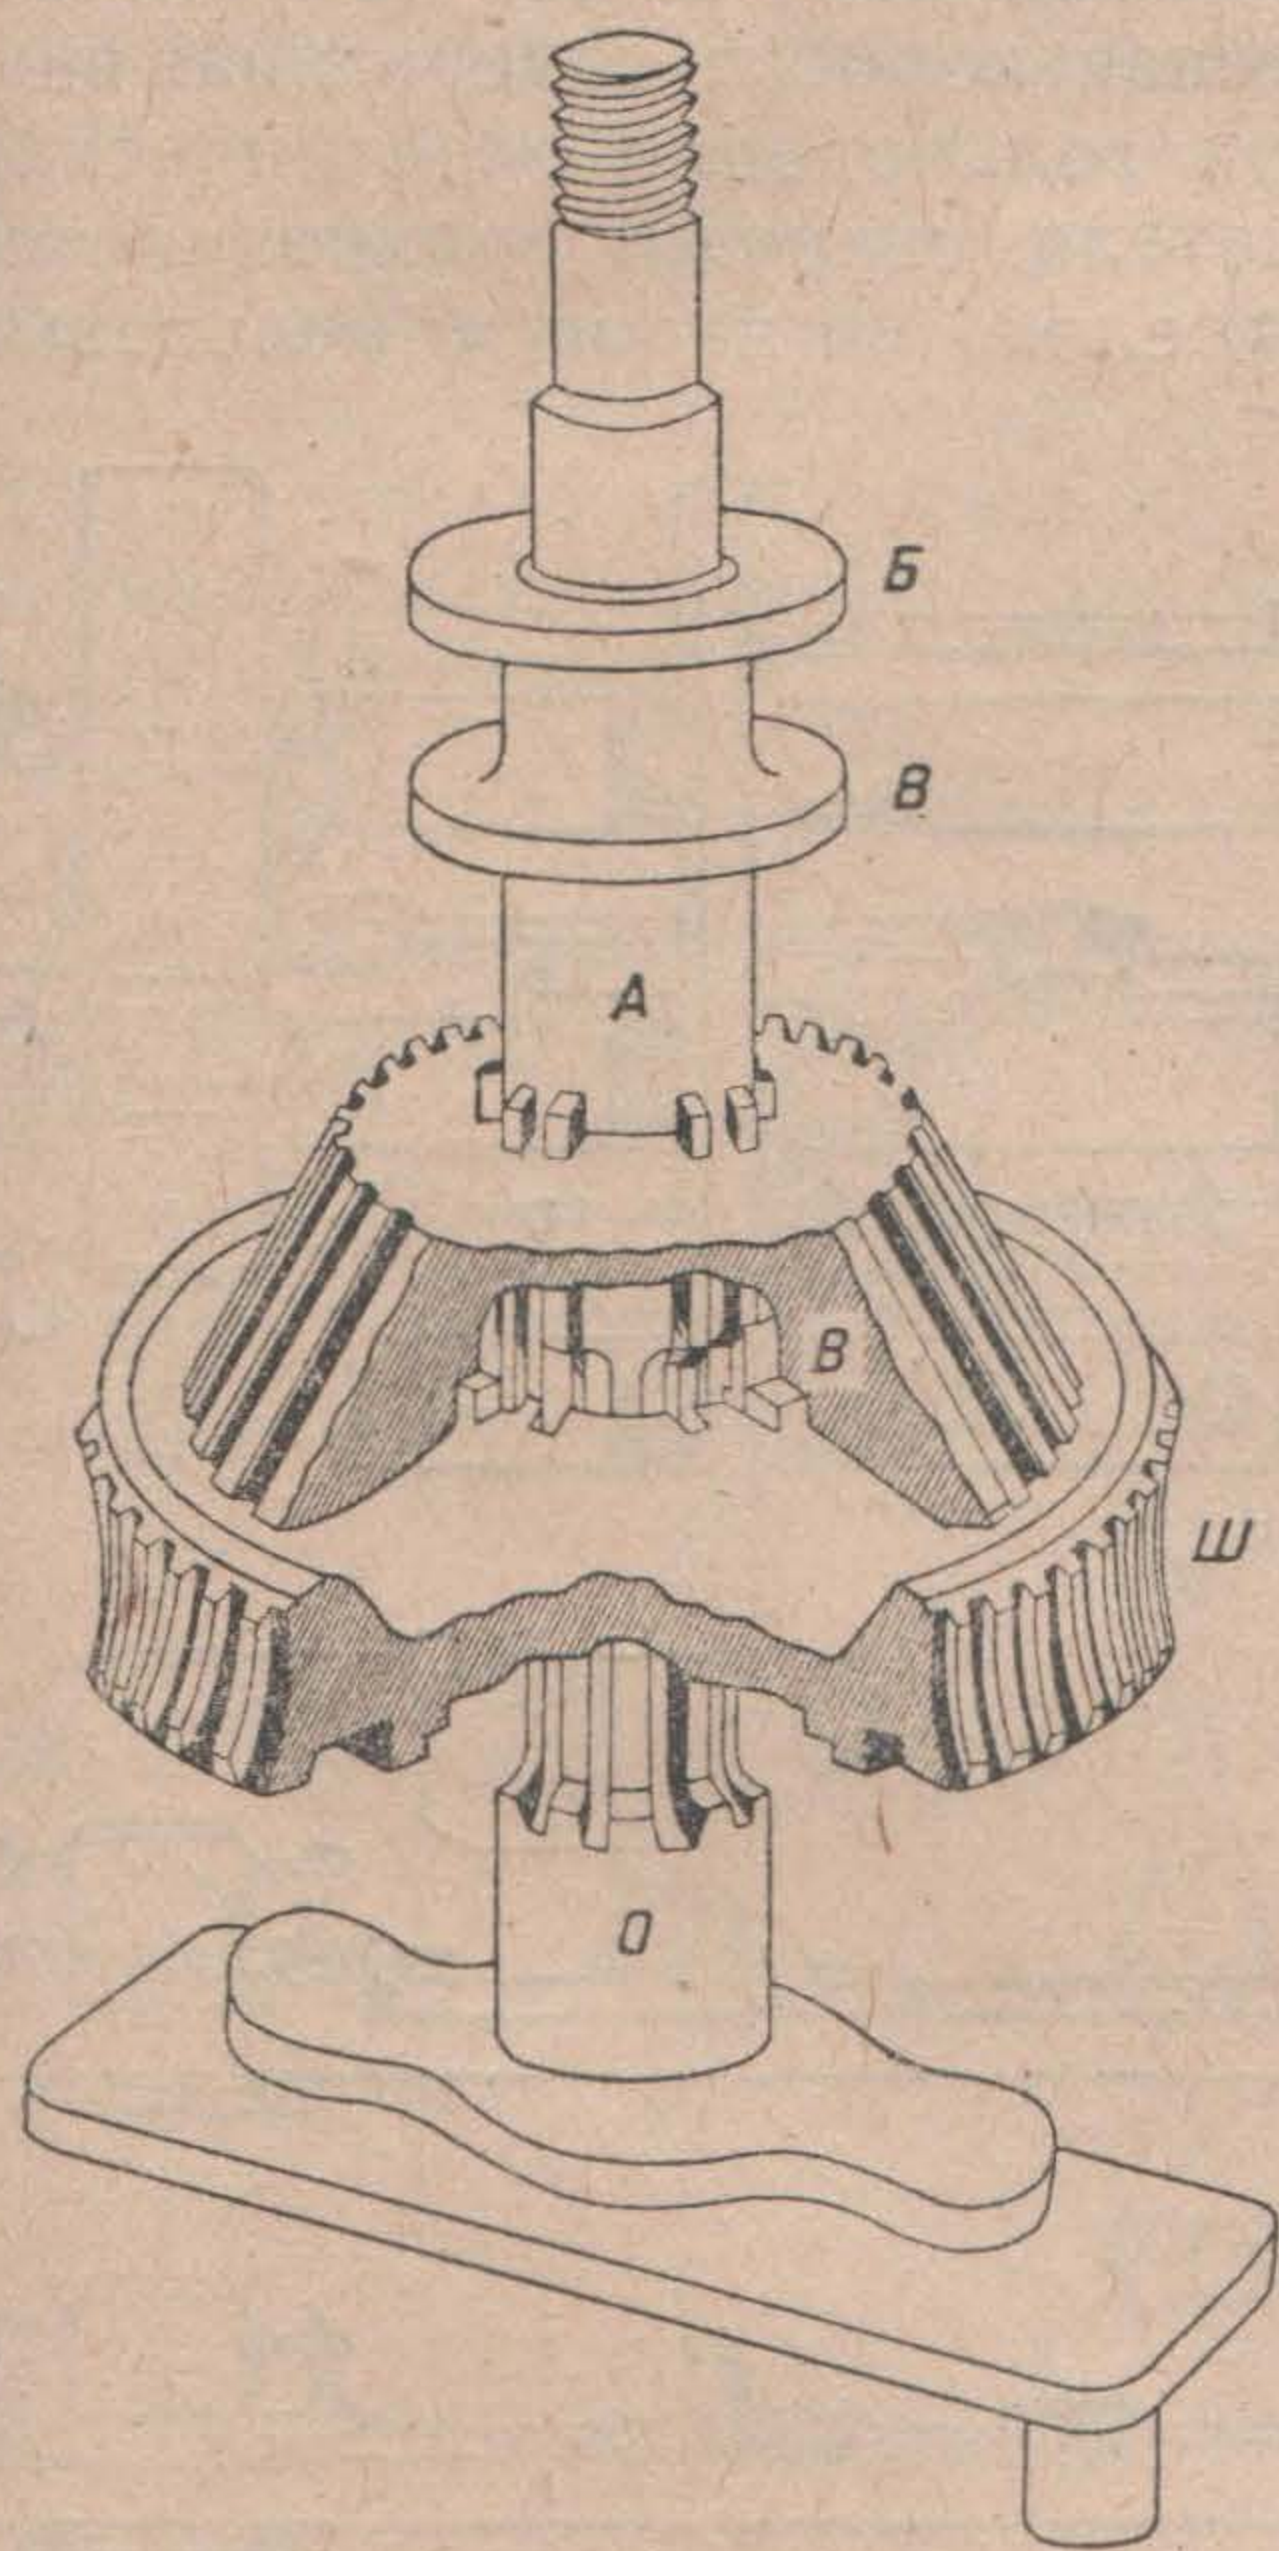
Главная рабочая ось с шестеренками при положении ручного перевода стрелки.
